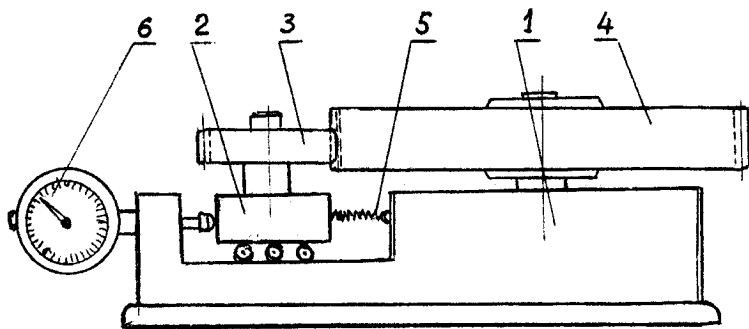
, а. Схема контрольного стенду для перевірки точності виготовлення зубчастих коліс.
